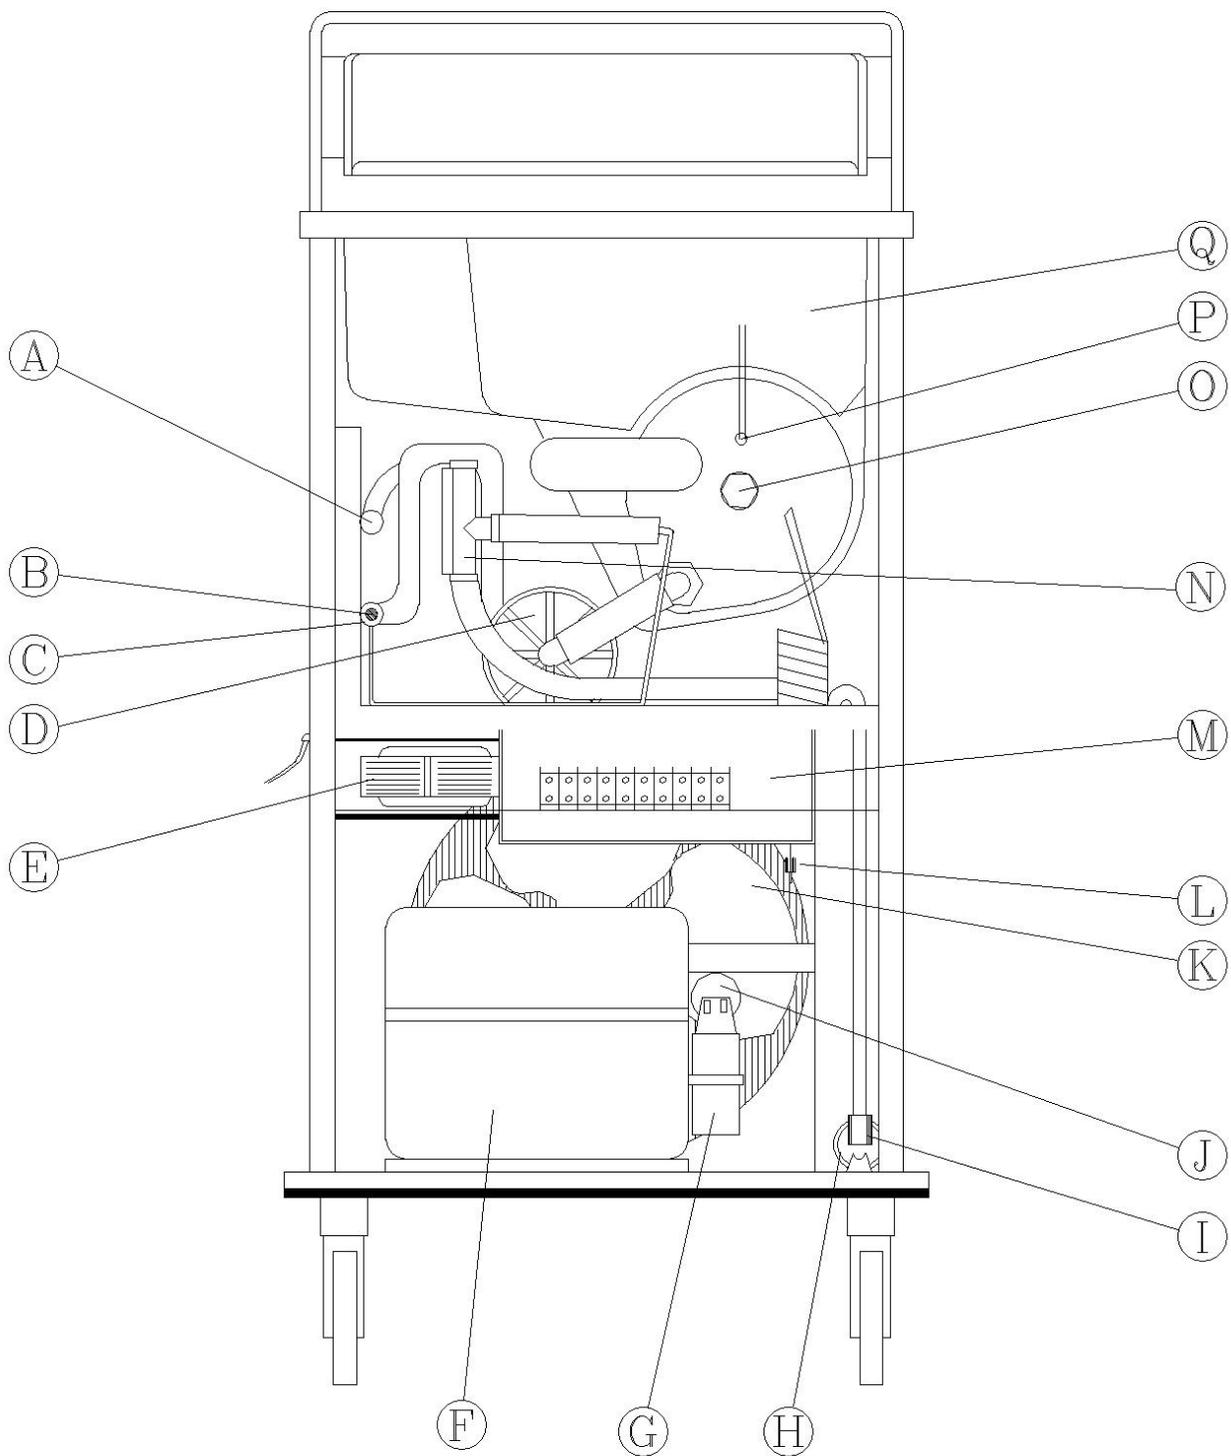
BLANKETROL III – VISTA POSTERIOR EXPUESTA
